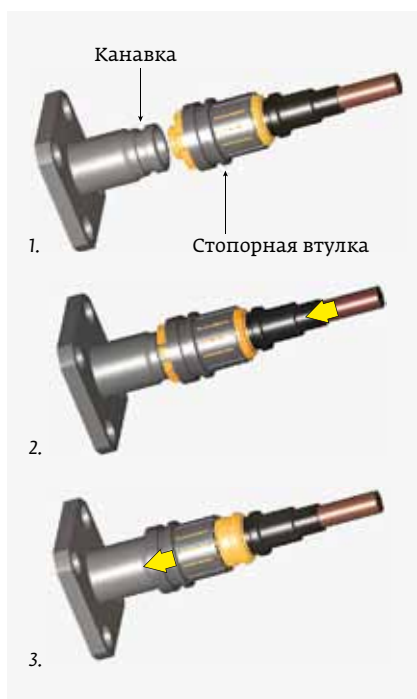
Этапы соединения розетки и вилки соединителей SMP-LOCK: 1 – исходное положение, 2 – образование соединения защелкиванием как в стандартных соединителях SMP, 3 – защелкивание стопорной втулки и блокировка соединения
